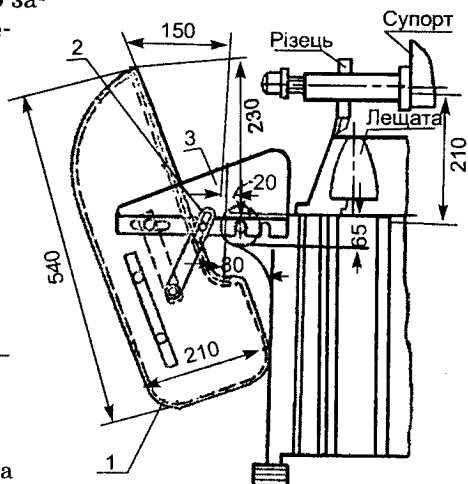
Знімний щиток до поперечно-стругального верстата:
